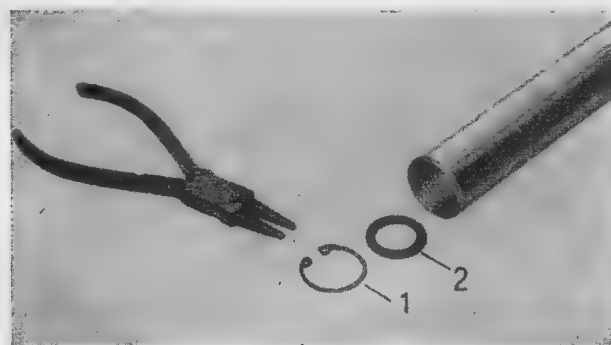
Anschlagsscheibe (2 mm dick) entfernen
